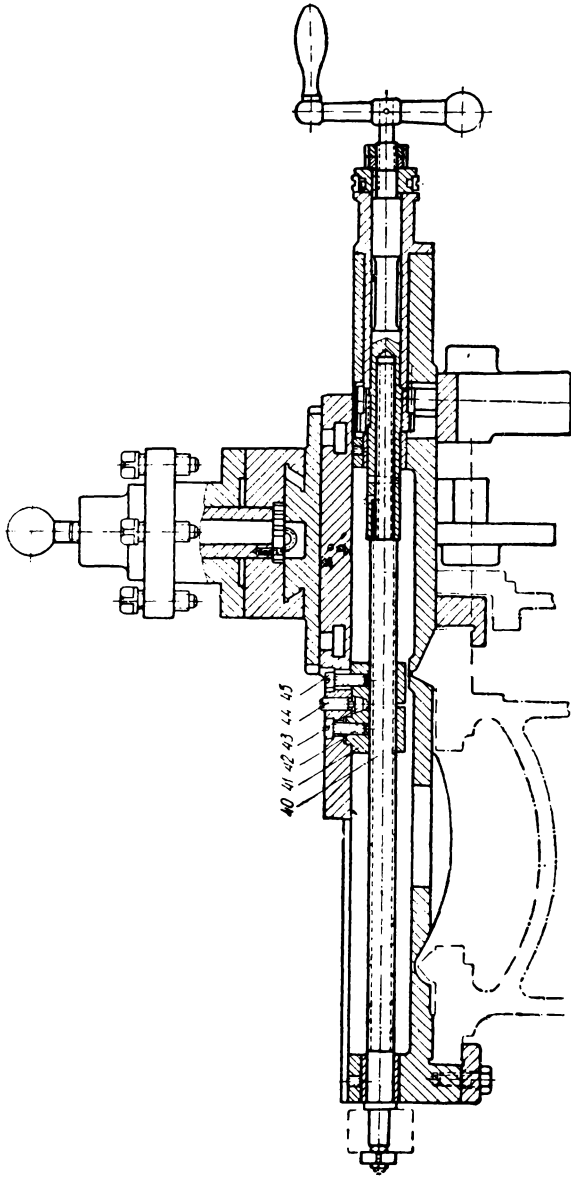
, а. Общий вид фартука токарного станка ДИП-200.
